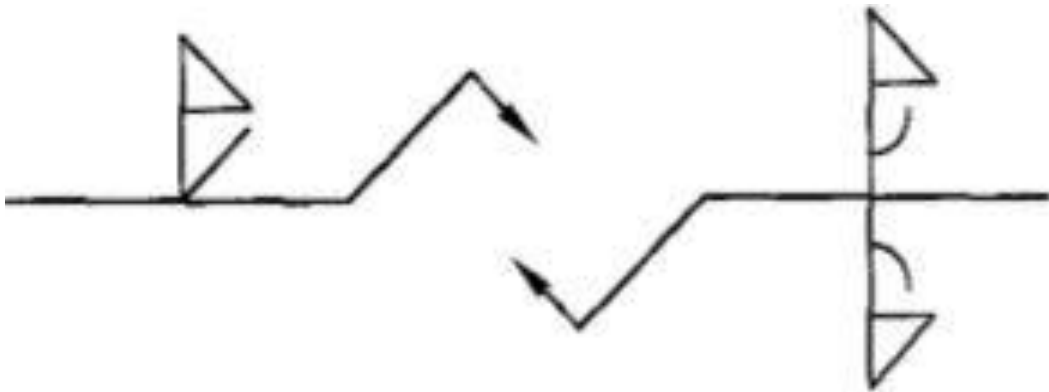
Combinaciones de Símbolos de Soldadura
